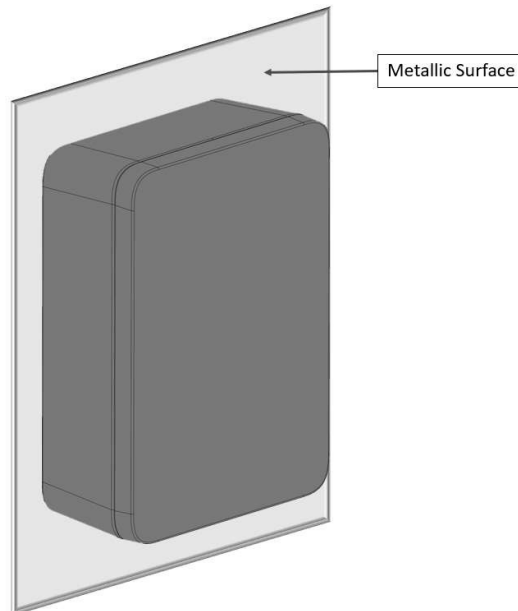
Befestigung des Gehäuses auf der Metalloberfläche
